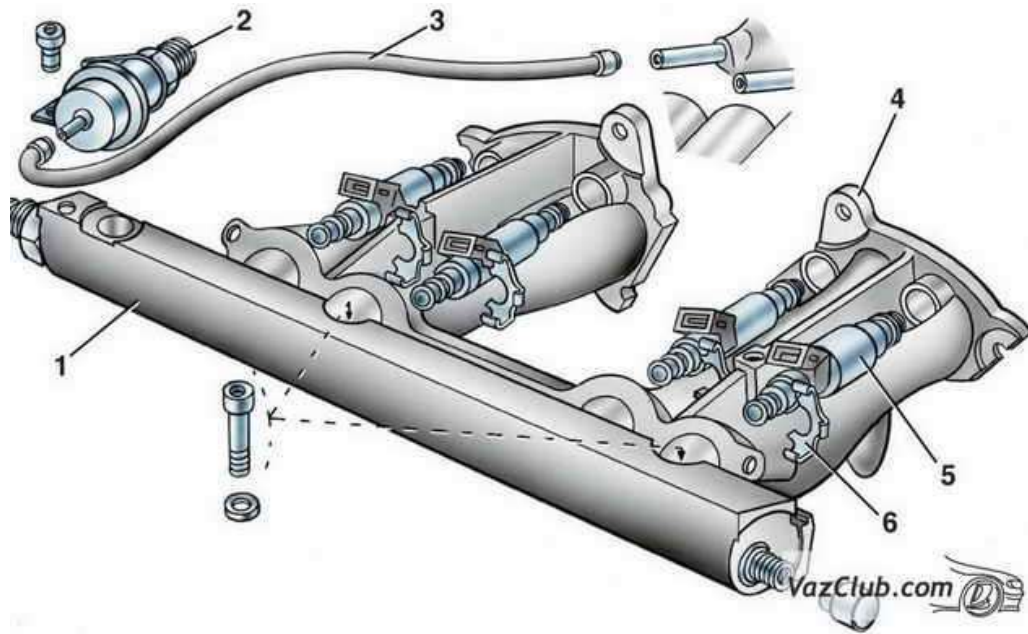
Снятие топливной рампы с форсунками: 1 – рампа форсунок; 2 – регулятор давления; 3 – вакуумный шланг; 4 – впускная труба; 5 – форсунка; 6 – защелка форсунки
